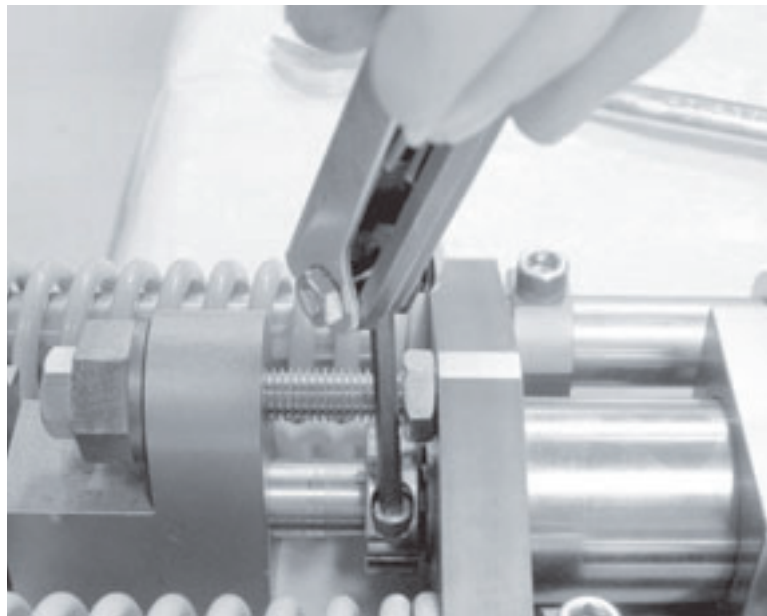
Отверните два винта блокиратора разрезного кольца.
